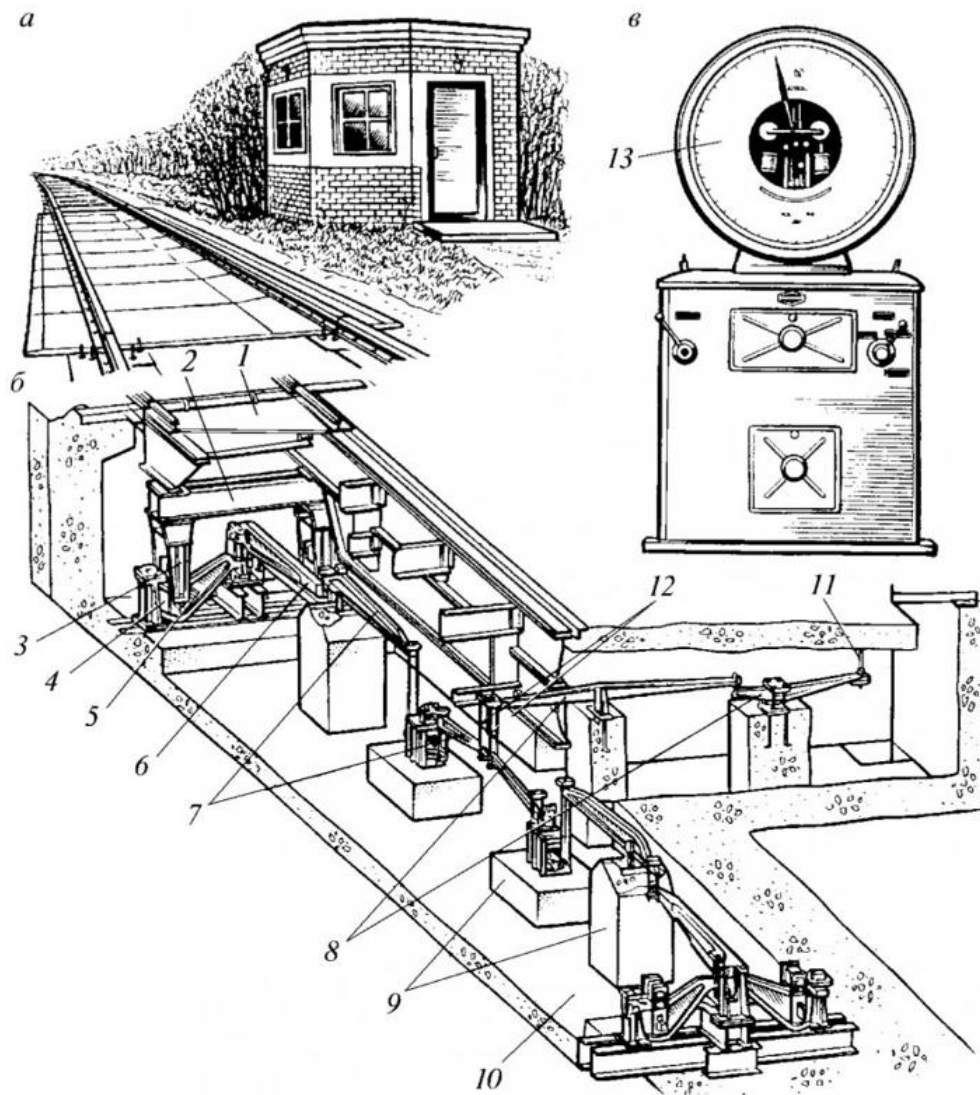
Вагонні ваги (ВЦ-150) із циферблатним вказівним приладом для статичного зважування: а – вагова споруда; б – механізм ваг, розташований у котловані; в – вказівний прилад
